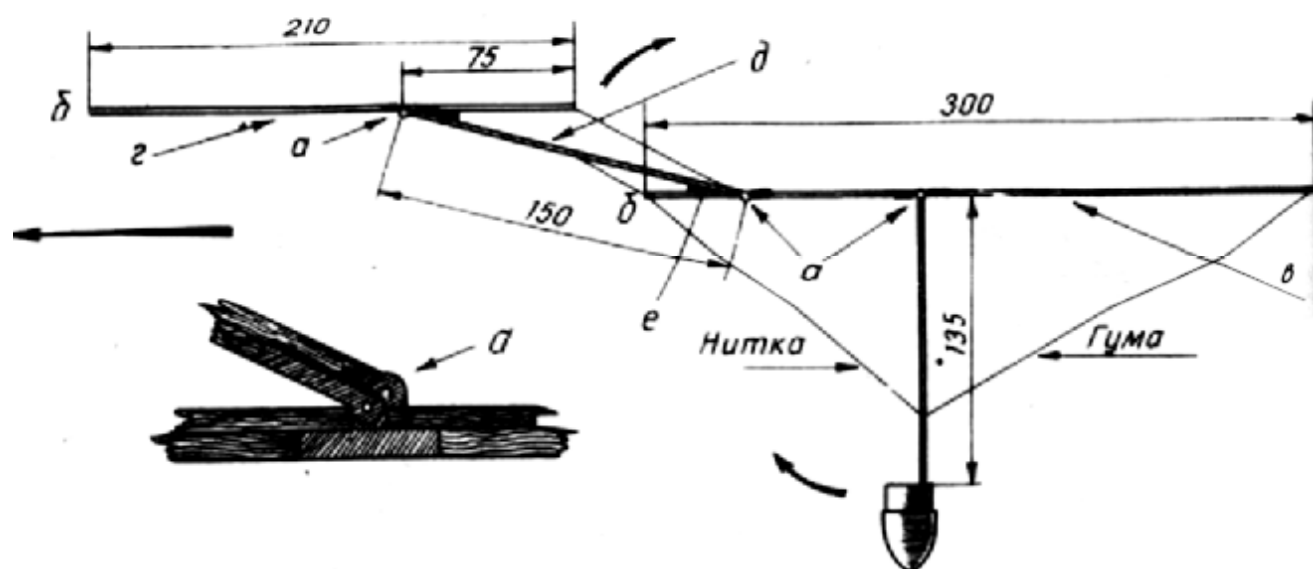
Модель ракетоплана типу «Качка» (вигляд збоку): а) вузли шарнірних кріплень; б) місця кріплень механізмів розкриття крила й стабілізатора; в) центрова нервюра крила; г) центрова нервюра стабілізатора; д) з'єднувальний кронштейн; е) липовий кутничок-обмежник.
